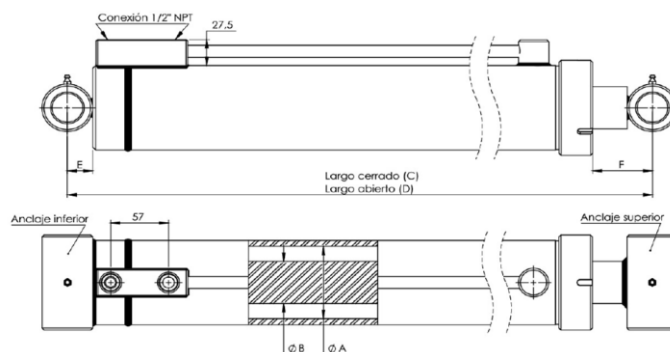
Características técnicas del cilindro hidráulico seleccionado. Cortesía de Moro Hidráulica.
